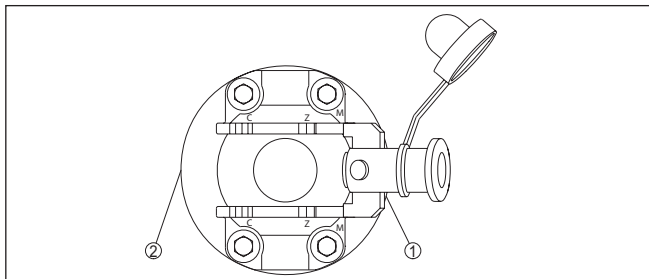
Montage-opstelling bij uitvoering met spoelaansluiting
